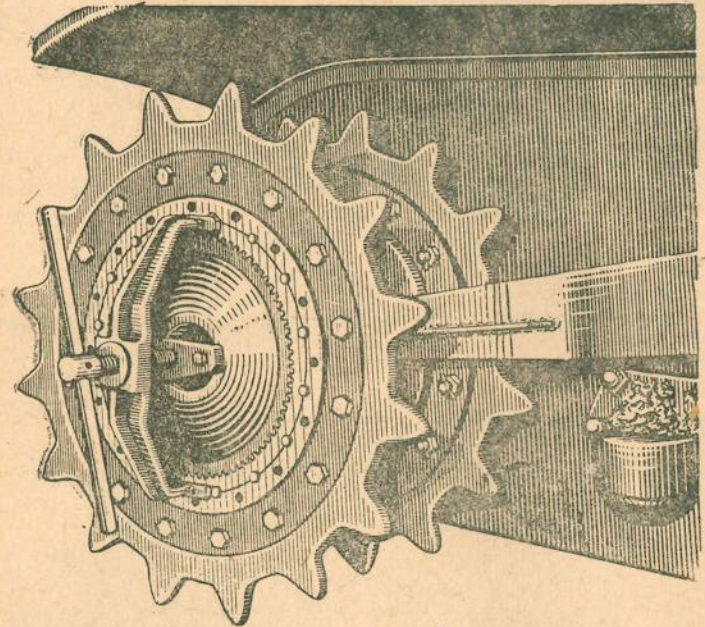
Выпрессовка ведущего вала при помощи приспособления № 4098
